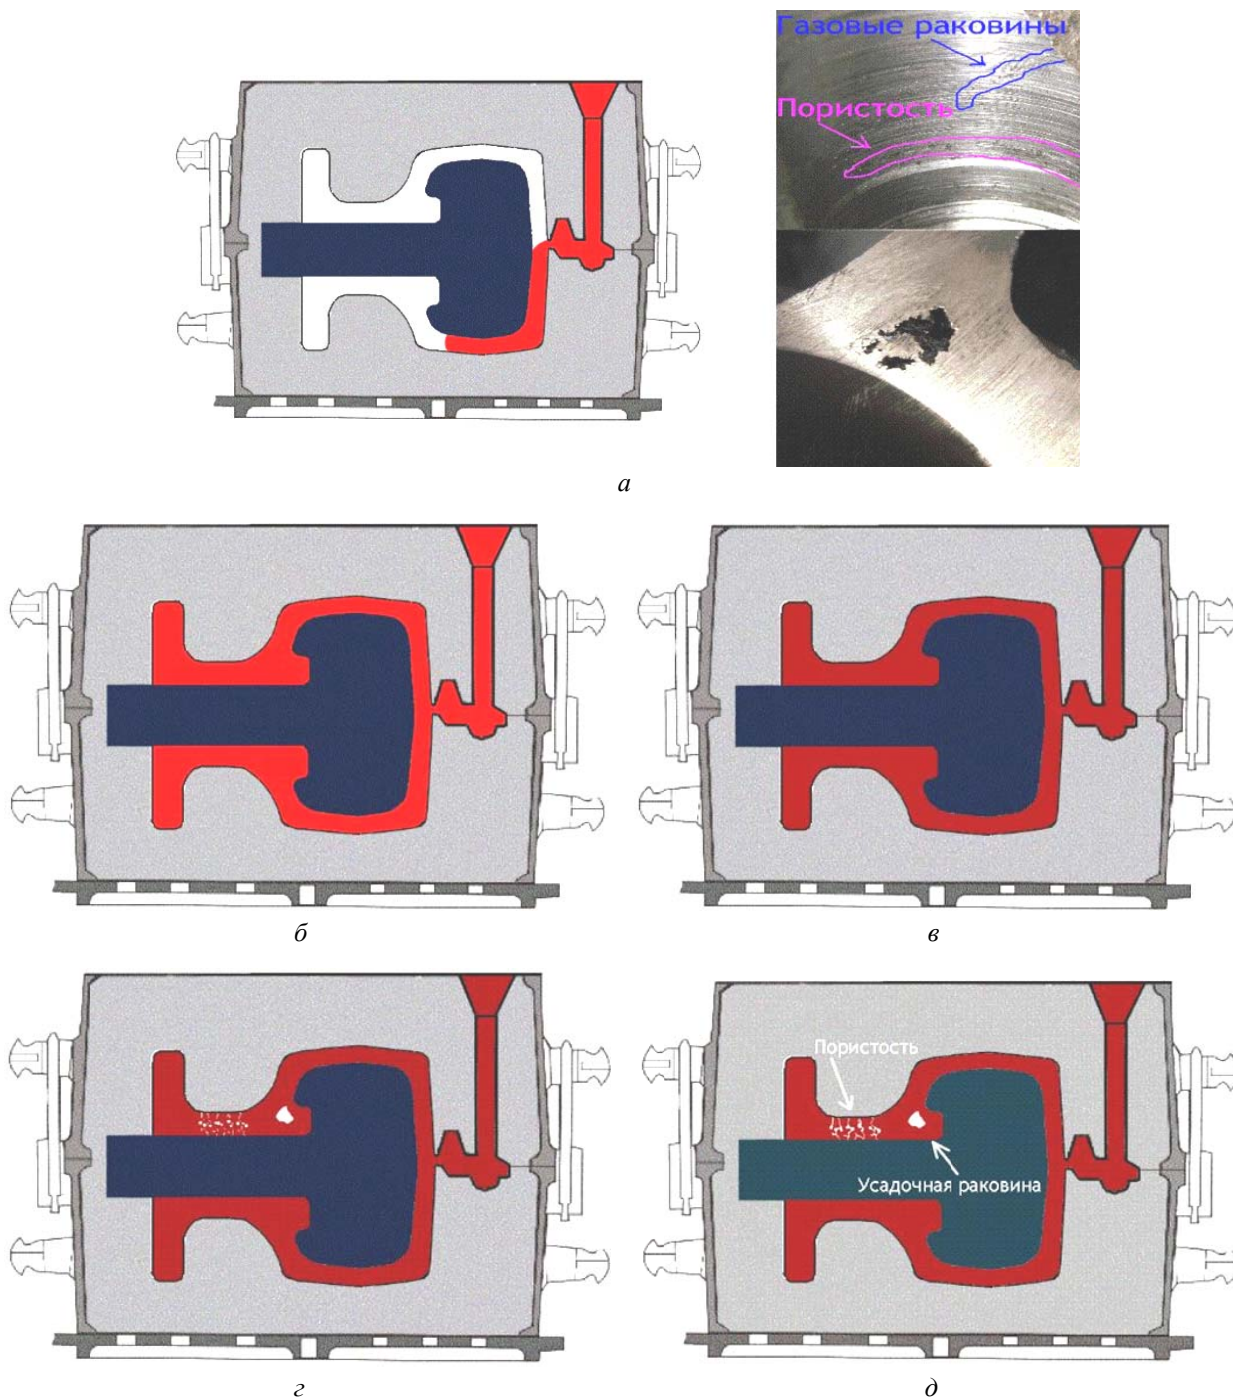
Форма в сборе без вентиляционных каналов, заливаемая сталью (а); завершение процесса заполнения формы металлом (б); процесс охлаждения металла, начало проникновения газовых раковин в тело отливки и образование усадочных дефектов (в); стадия образования газовых и усадочных дефектов в отливке (г); стадия завершения образования газовых и усадочных дефектов в отливке (д)
